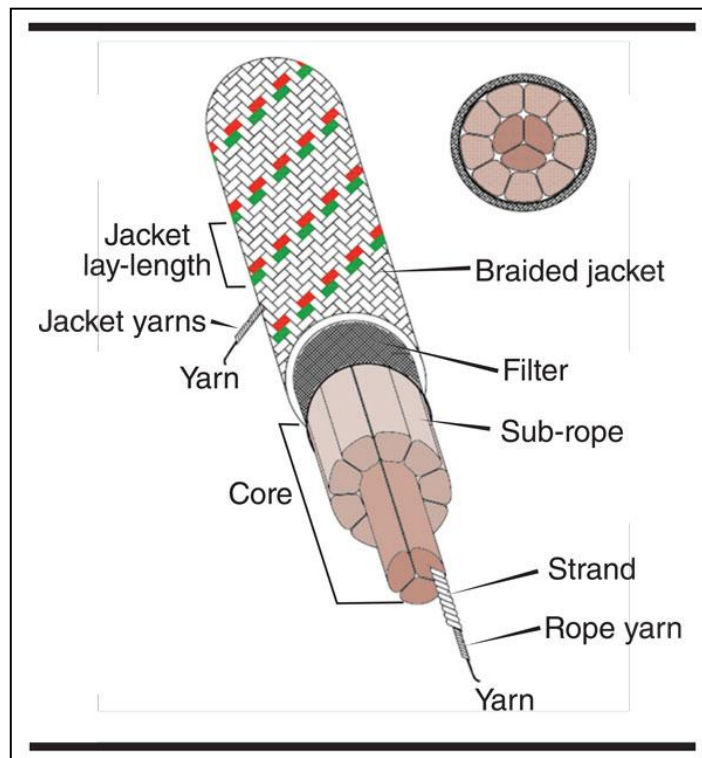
Vista e corte da secção transversal do CP GAMA 98®⁶⁴.
